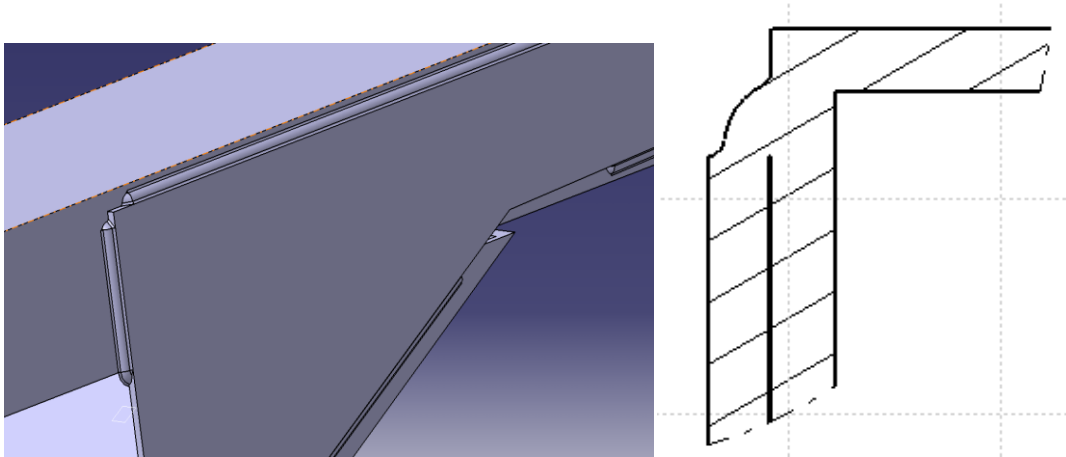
Modèle CAO du cordon de soudure
